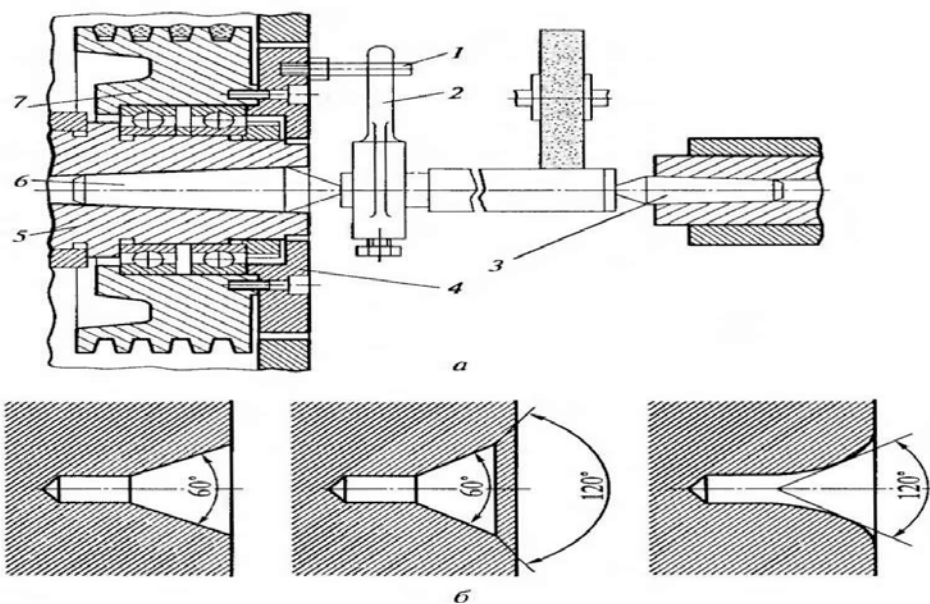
Схема установки заготовки в упорных центрах круглошлифовального станка (а) и формы центровых отверстий на заготовках (б):
